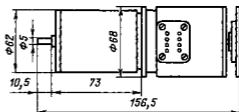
30 Габаритные и установочные размеры двигатель-генераторов СМА, СМБ, СМВ
